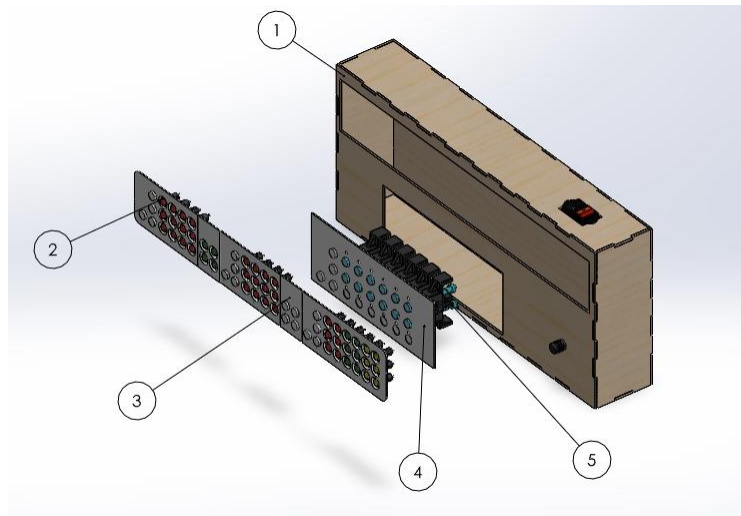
Diseño de la propuesta seleccionada en vista explosionada.
